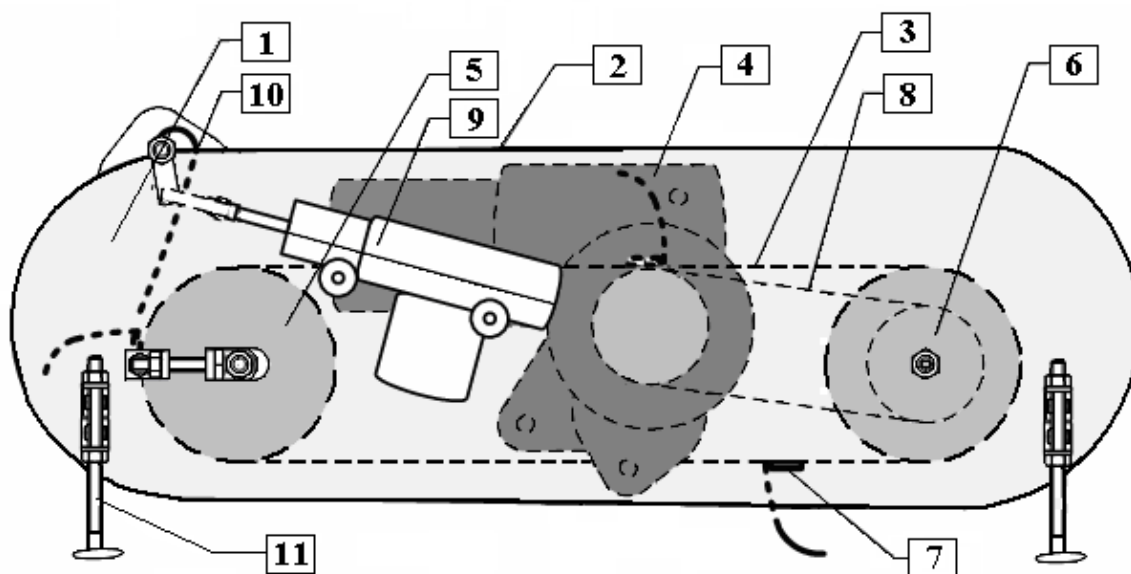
Конструктивная схема механического ленточного устройства для вычесывания пуха коз: 1 – пластина; 2 – верхняя крышка; 3 – рабочая лента; 4 – электропривод; 5 и 6 – шкивы; 7 – планки с вычесывающими элементами; 8 – зубчатый ремень; 9 – привод; 10 – снимающая гребенка; 11 – ограничитель.
